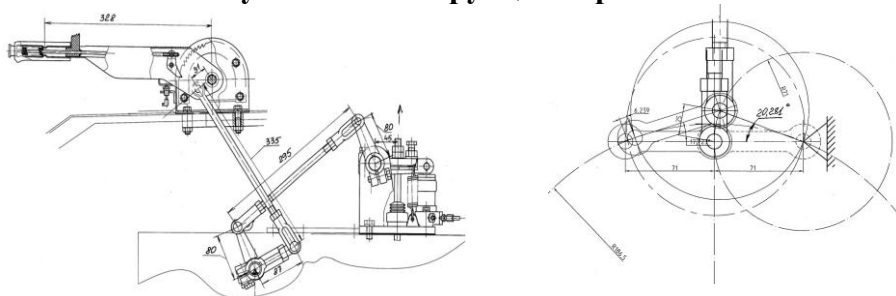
Конструкция привода стояночно-запасного тормоза
